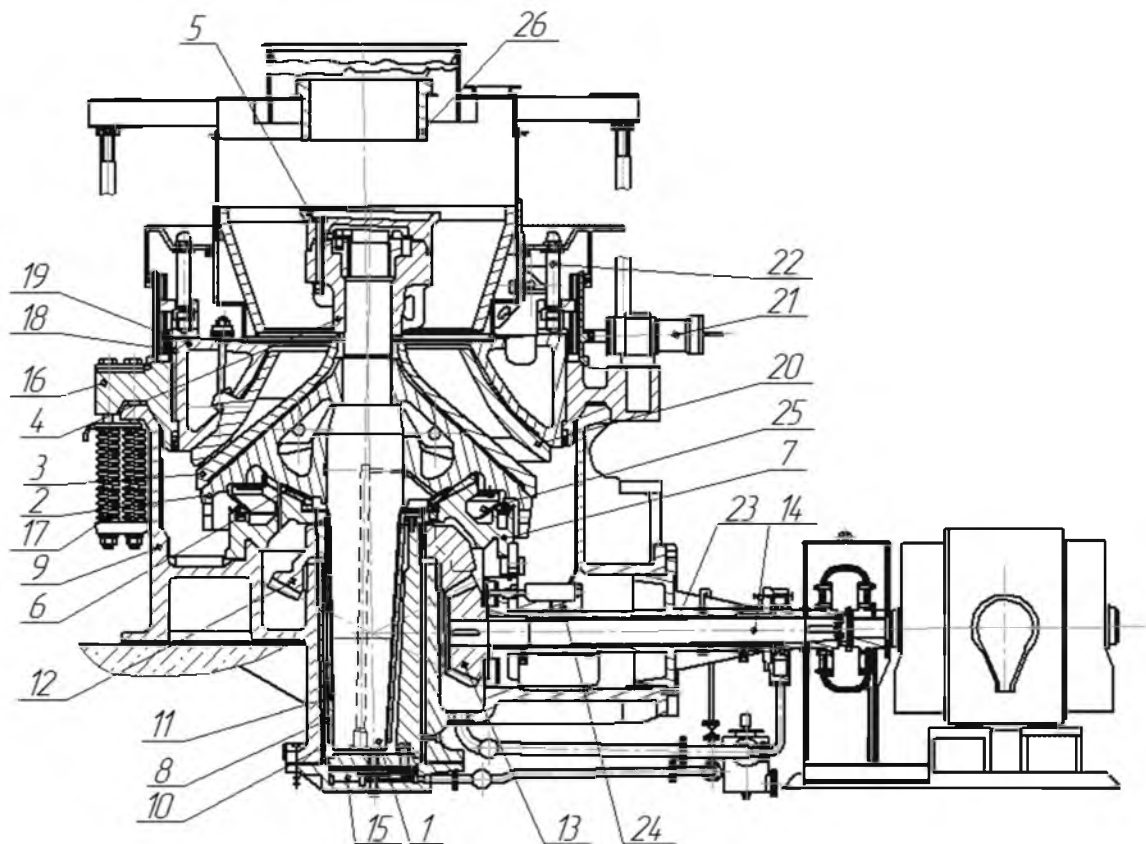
Загальний вид конусної дробарки середнього дроблення КСД-2200
